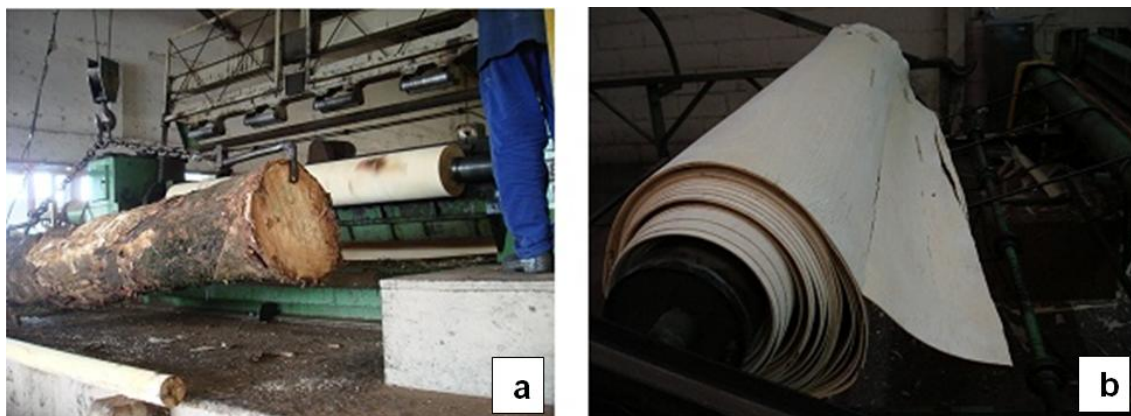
Laminação das toras: (a) torno industrial; (b) bobina, tora desenrolada
